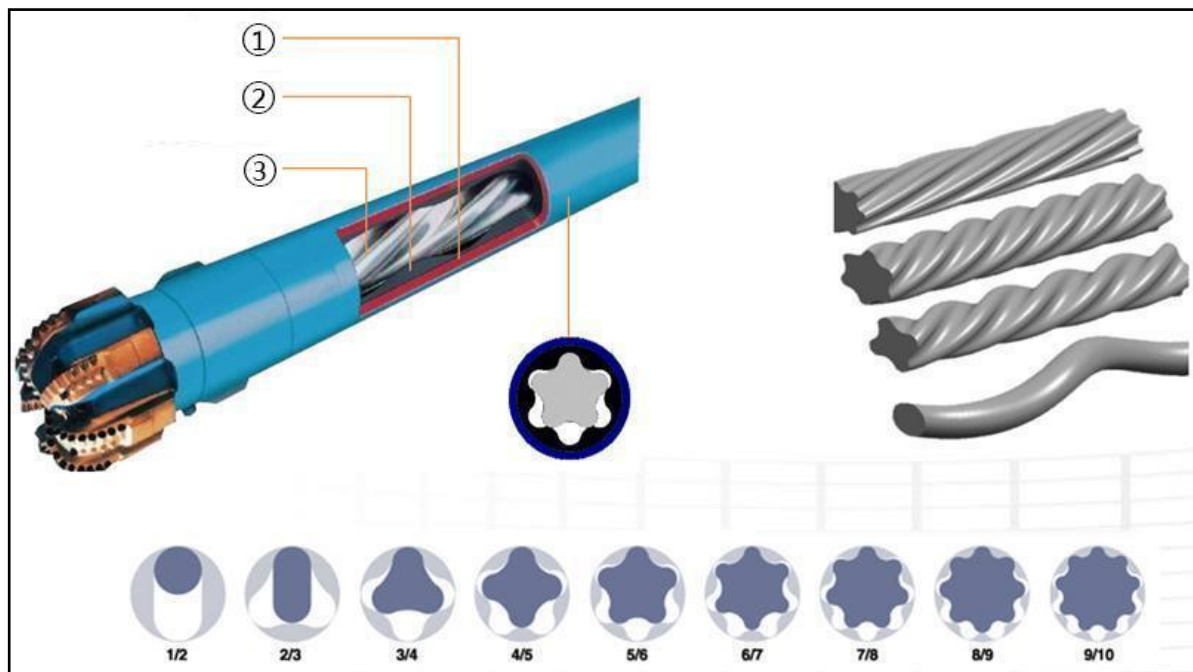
Motor de fondo, Weifan Subtor Rotating Precision Machinery CO.
